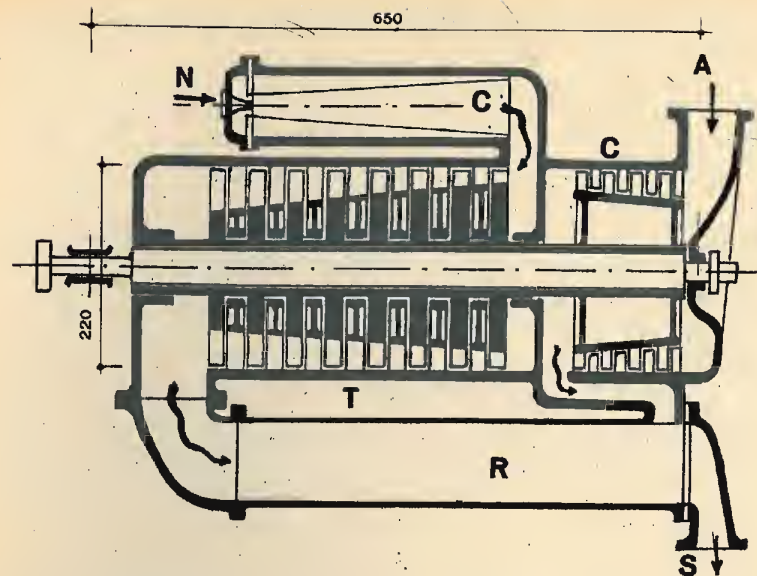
Sezione schematica d'una turbina a combustione interna: A ingresso aria; B compressore; T turbina coassiale; C camera di combustione; N iniettore del combustibile; R riscaldatore dell'aria; S scarico del gas.
